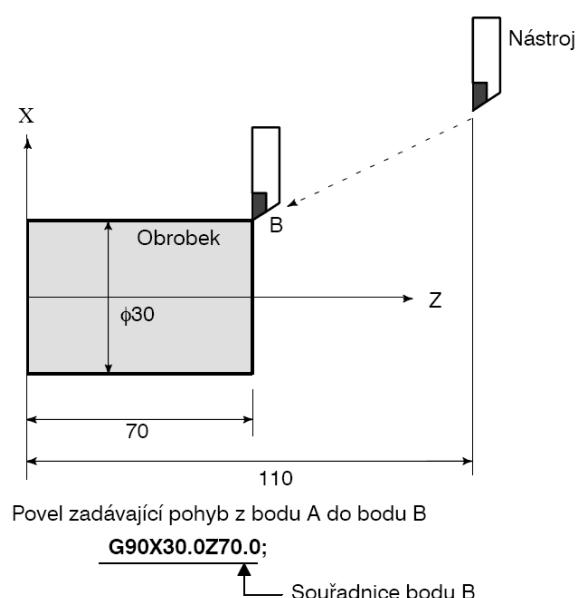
Souřadný systém určený CNC systémem [9]
